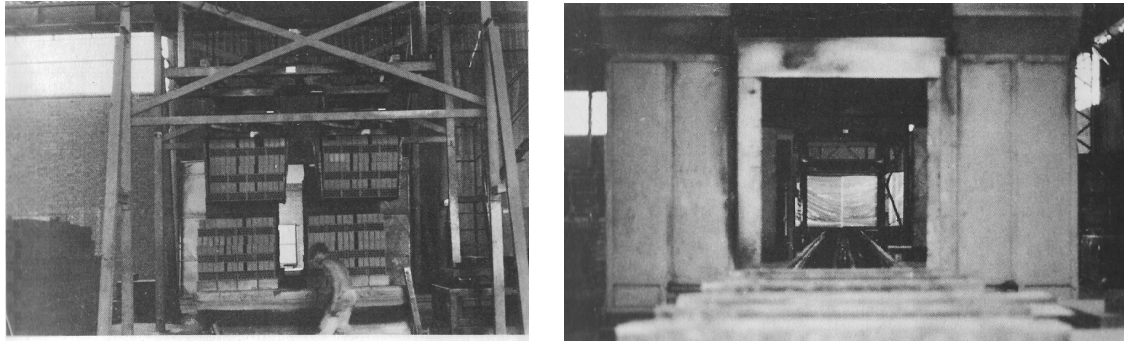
p Dos vistas de la desapiladora y empaquetadora del material.
